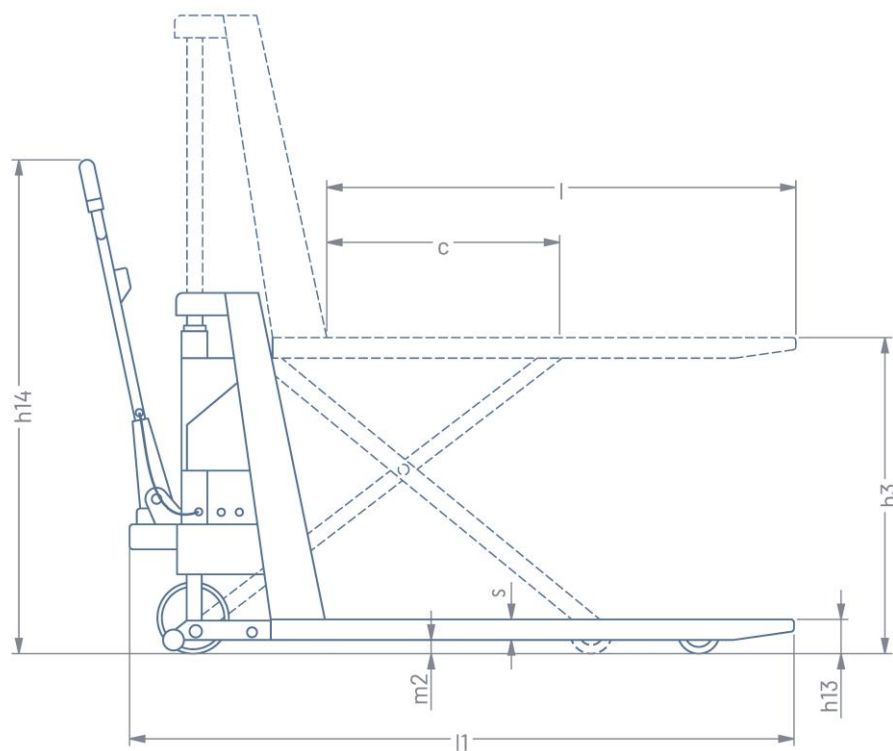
ZAC-S &amp; ZAC-E Seitenansicht mit Kürzeln
